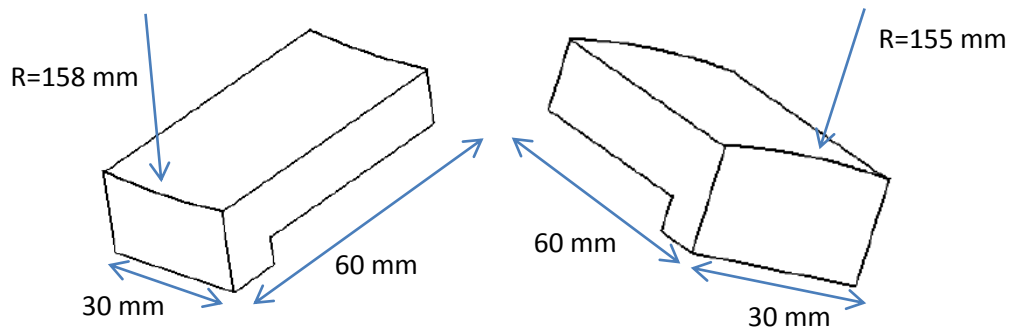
Mors de forme utilisés pour le serrage des éprouvettes courbes.
